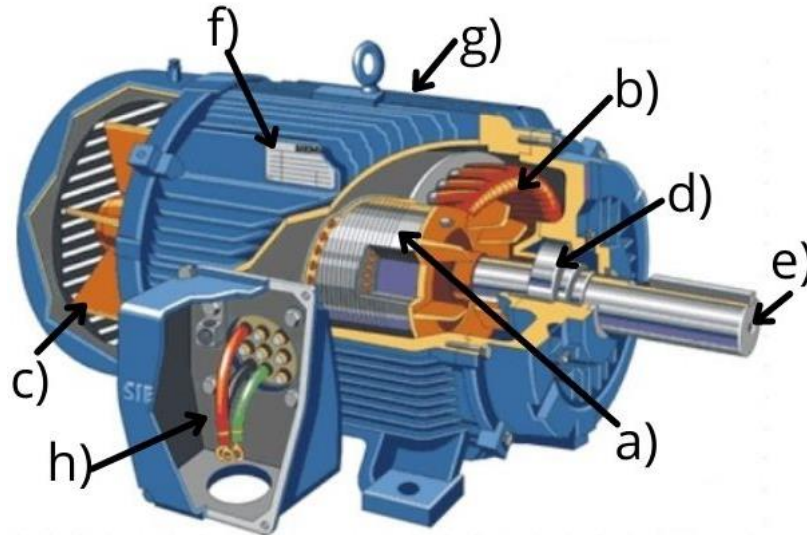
Partes del motor a) Rotor b) Estator c) Ventilador d) Rodamiento e) Eje f) Placa de datos g) Carcasa h) Caja de bornes (Autoría Propia).
